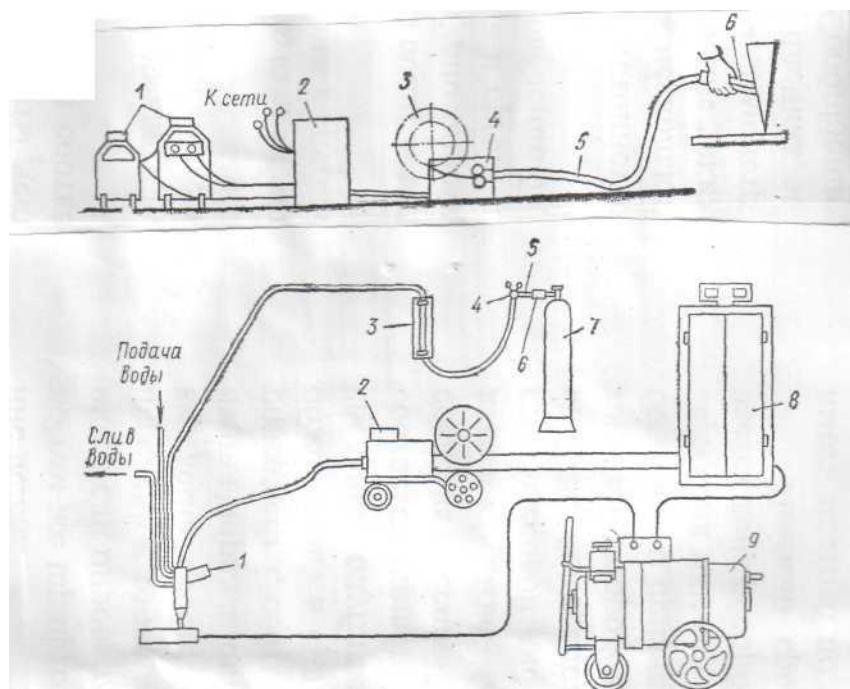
Схема полуавтоматической установки для сварки в углекислом газе
